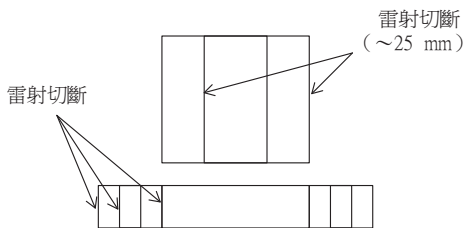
使用於雷射切斷、焊接、精修的切削加工的案例
